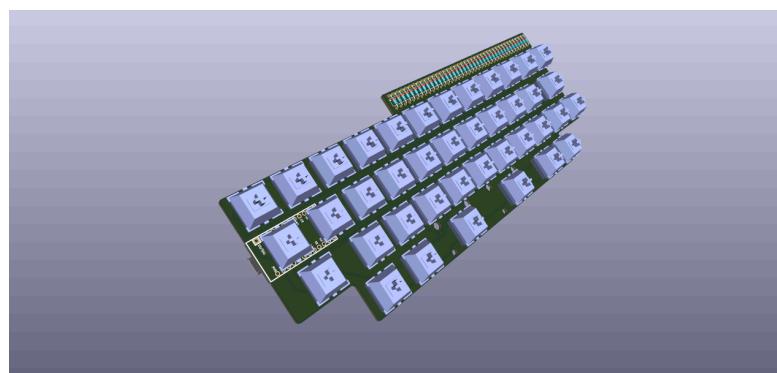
Representação frontal 3D da PCB dos teclados TCBK40 no Kicad
